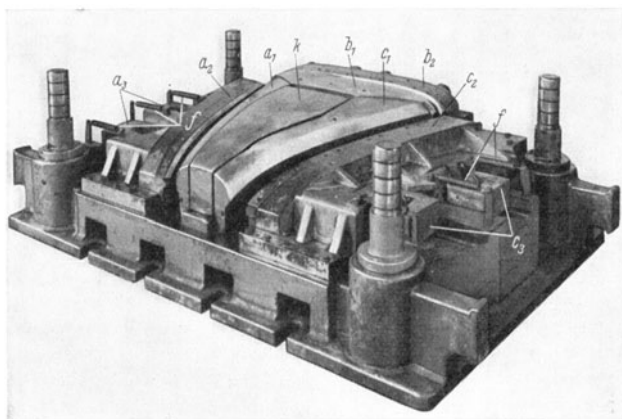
Umkantwerkzeug für unterschrittene Biegungen
